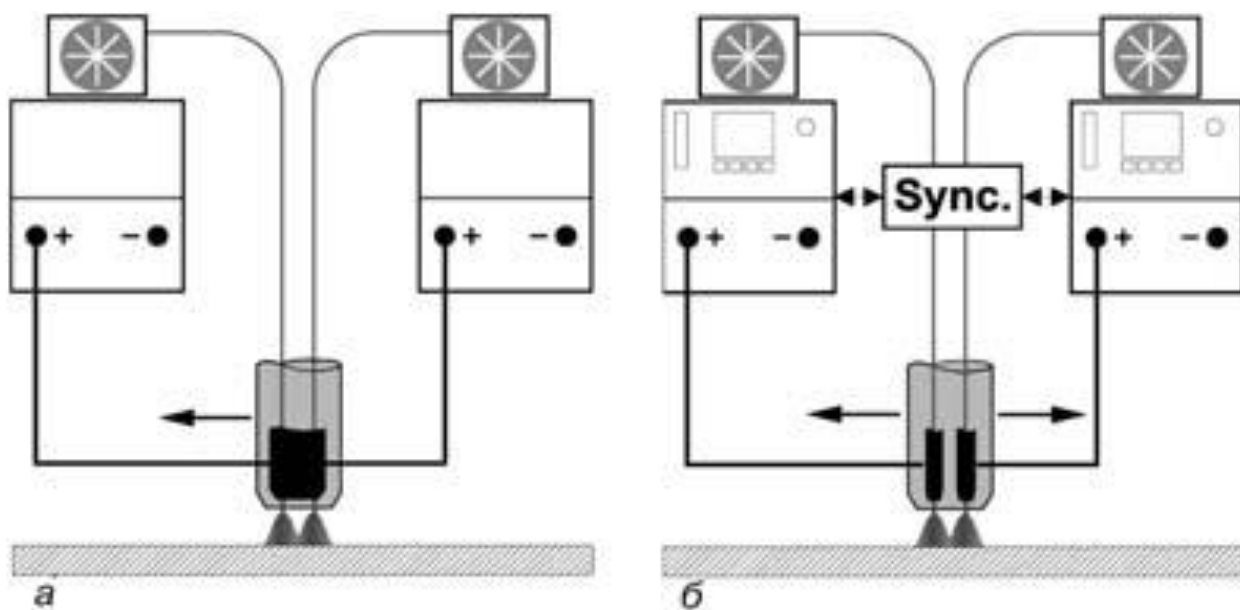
Принципиальные схемы сварки двумя проволоками с общим (а) и отдельным (б) токоподводом
